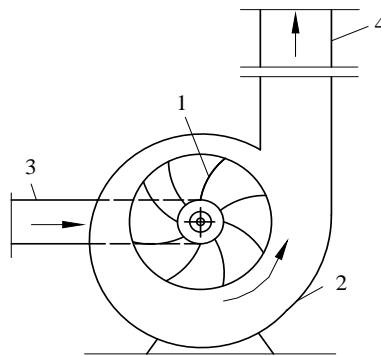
Побудова відцентрового насоса: 1 – робоче колесо; 2 – корпус; 3 – всмоктувальний патрубок; 4 – напірний трубопровід
